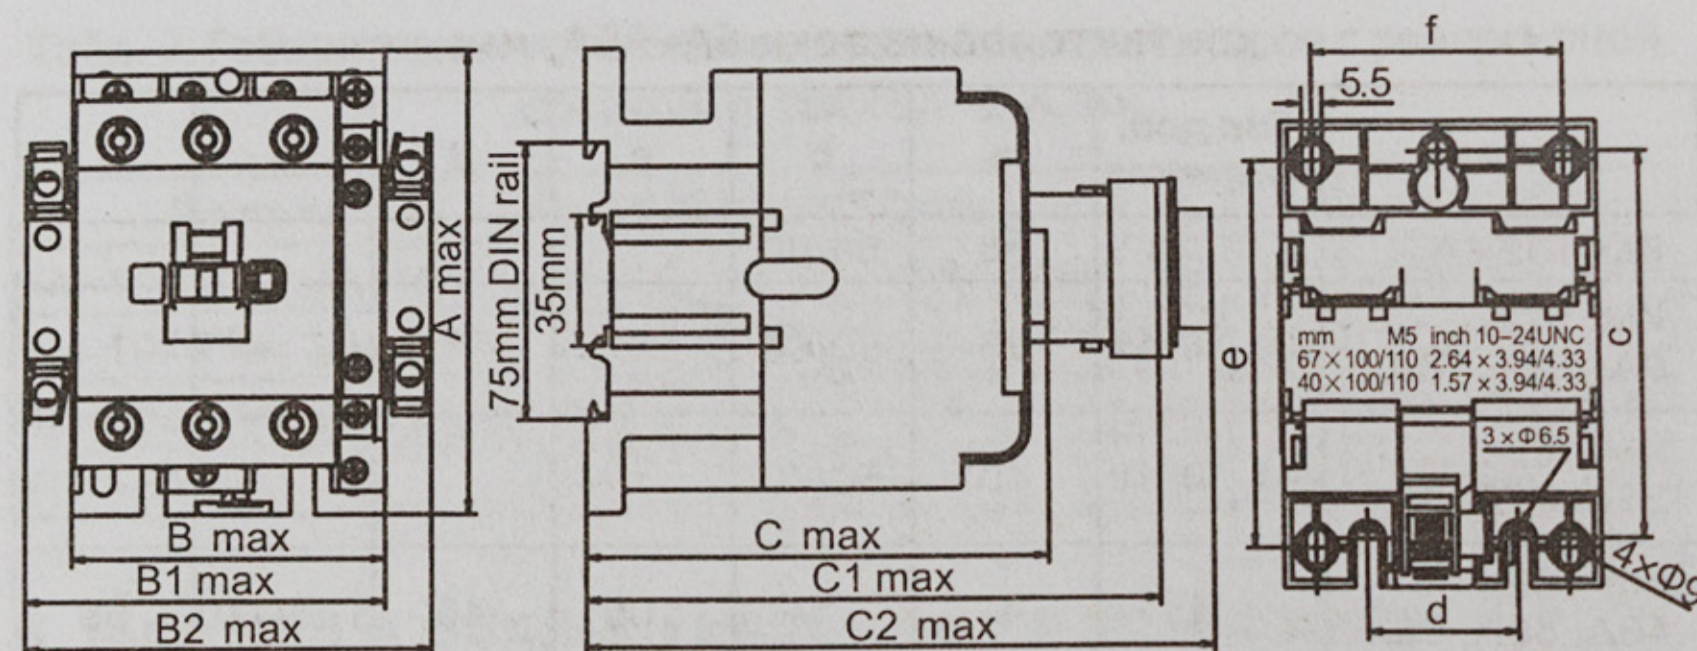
Габаритные и установочные размеры контакторов на токи 40А–95А, мм.
